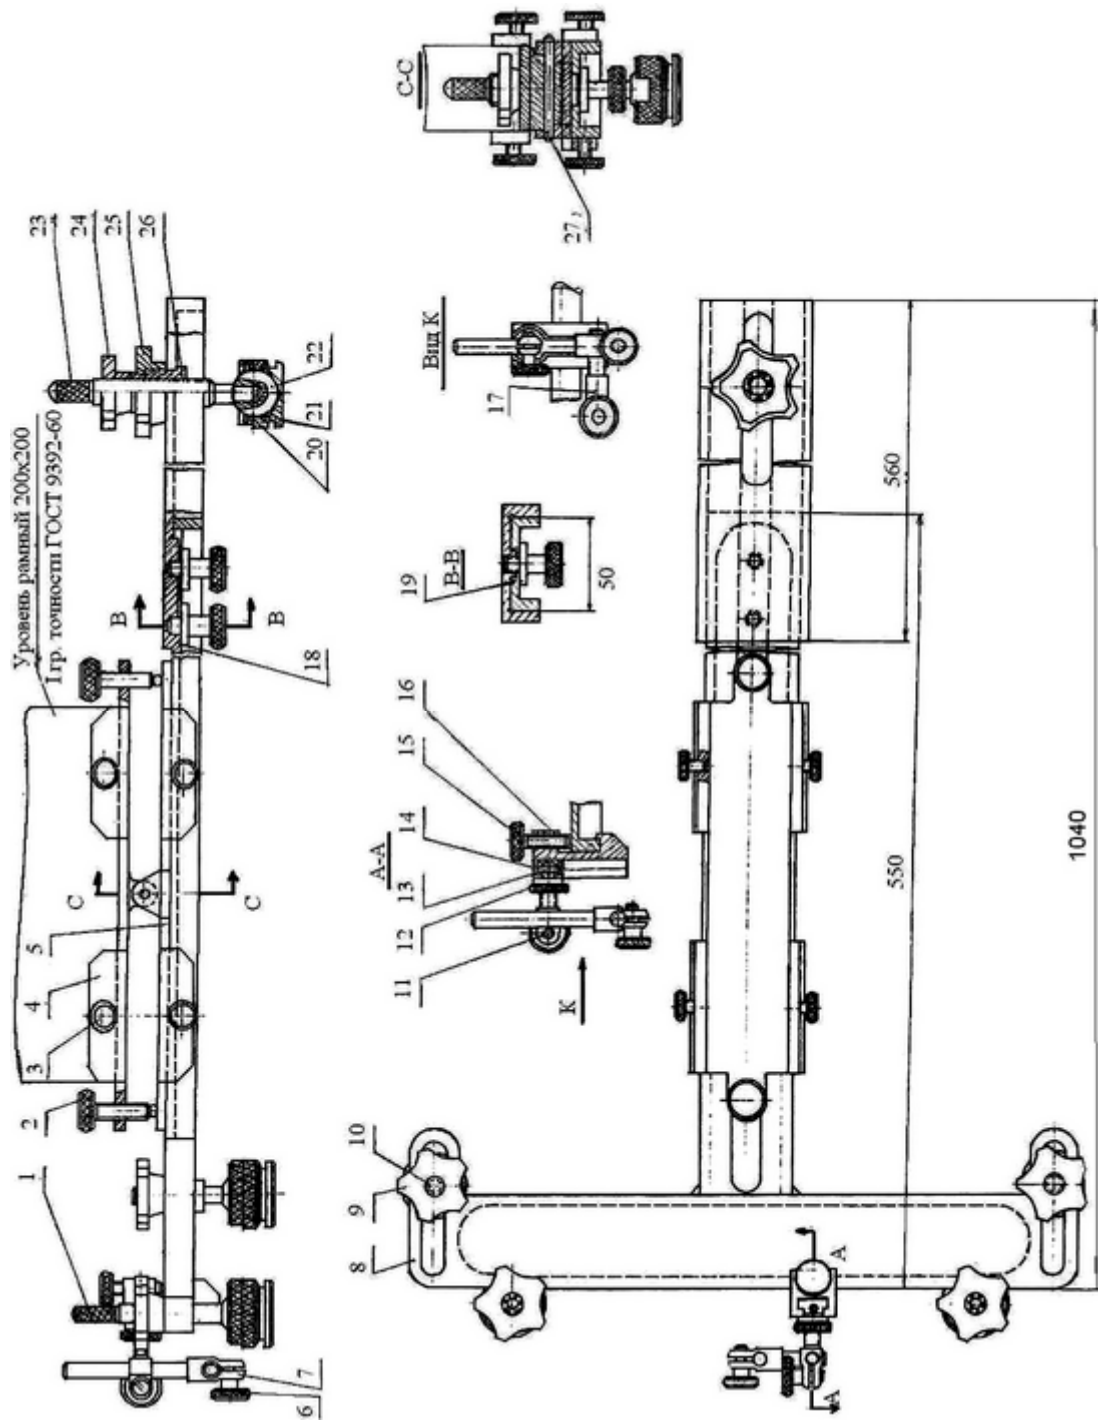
Приспособление для проверки направляющих станины (универсальный мостик)
